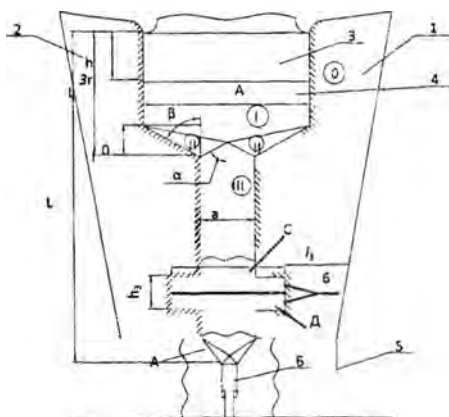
Схема скоростного выдавливания биметаллической стержневой детали «Выталкиватель» с формообразующей рабочей поверхностью
